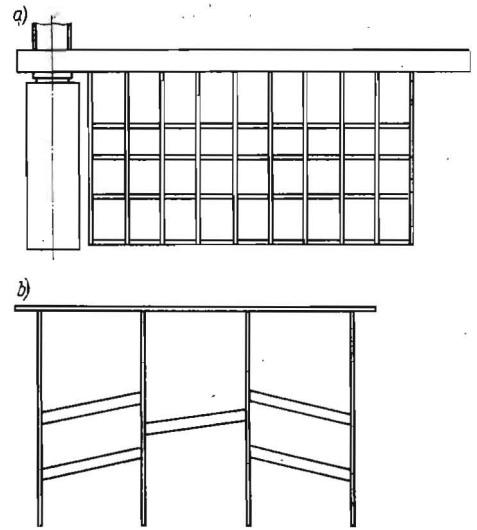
Ansicht der untersuchten Rührkörperformen; a) engmaschiger Rührkörper, b) weitmaschiger Rührkörper
